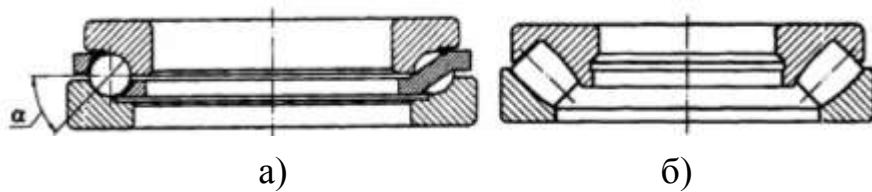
Упорно-радиальные шариковые и роликовые подшипники
